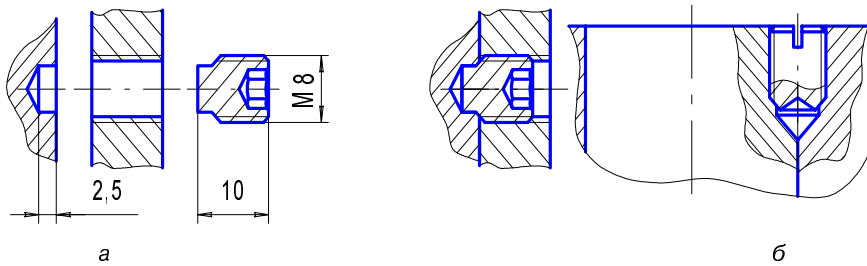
Установочный винт: а — отверстия под установочный винт; б — примеры установки
